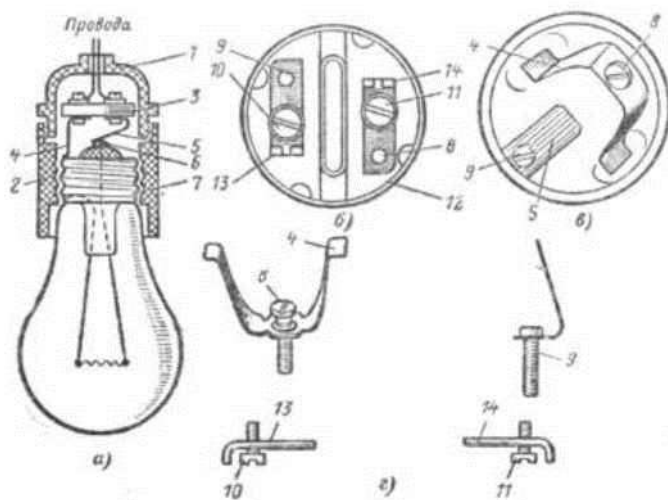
Устройство резьбового патрона марки Р-27: а — внешний вид патрона 1, 2 — свинчивающиеся части; 3 — вкладыш; 4, 5 — контакты; 6 — центральный контакт; 7 — гильза цоколя лампы; б — вид вкладыша со стороны контактов 8, 9 — винты; в — вид вкладыша со стороны винтов 10 и 11; вкладыш — 12; пластины — 13, 14; г — детали разобранного вкладыша
